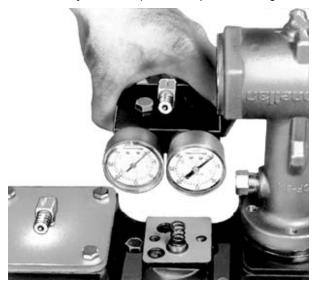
Conjunto do posicionador Observe agora que o posicionador (147) e a gaxeta (146) estão orientados.
